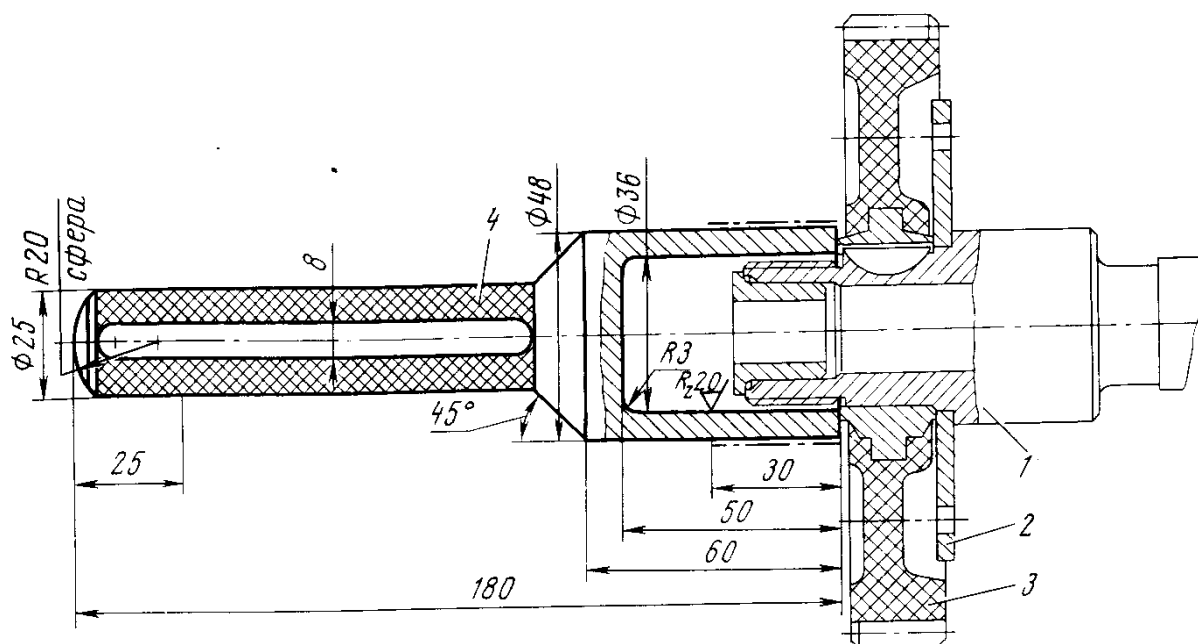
Оправка для напрессовки шестерни распределительного вала: 1 — распределительный вал; 2 — фланец распределительного вала; 3 — шестерня распределительного вала; 4 — оправка
